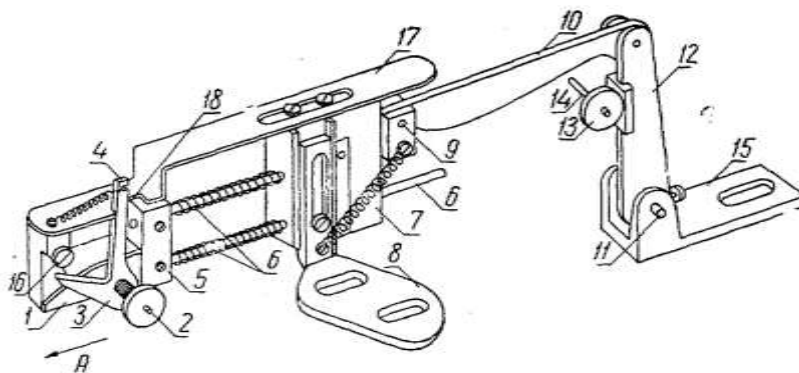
Пристрій для котельної машини для автоматичної обрізки ланцюжка шва
